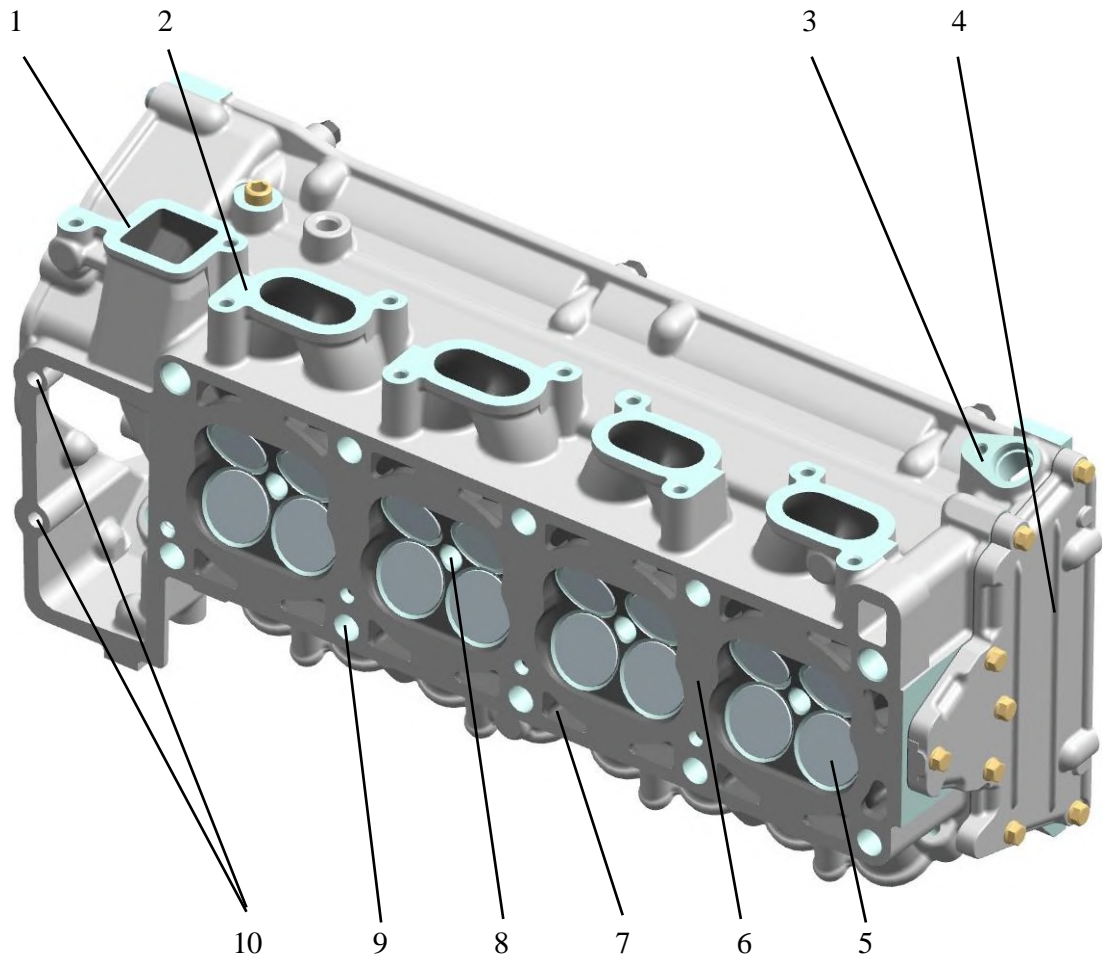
Zylinderkopf. Ansicht auf die Brennräume, den Auspuffkrümmerflansch und die hintere Abdeckung:
